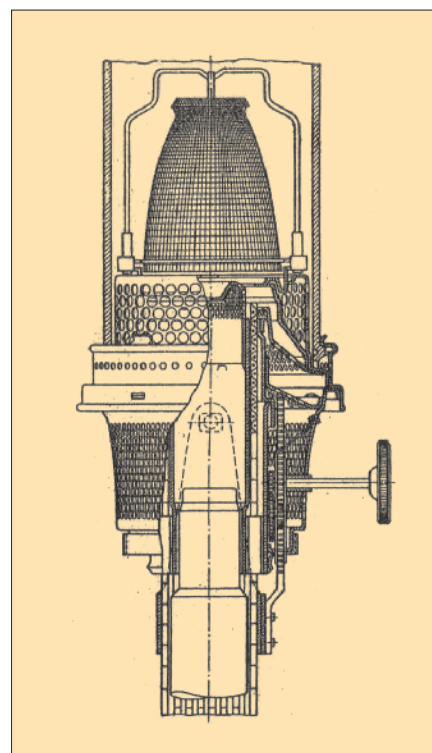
Univerzální závěsná i stolní petrolejová lampa asi z 20. let 20. století
